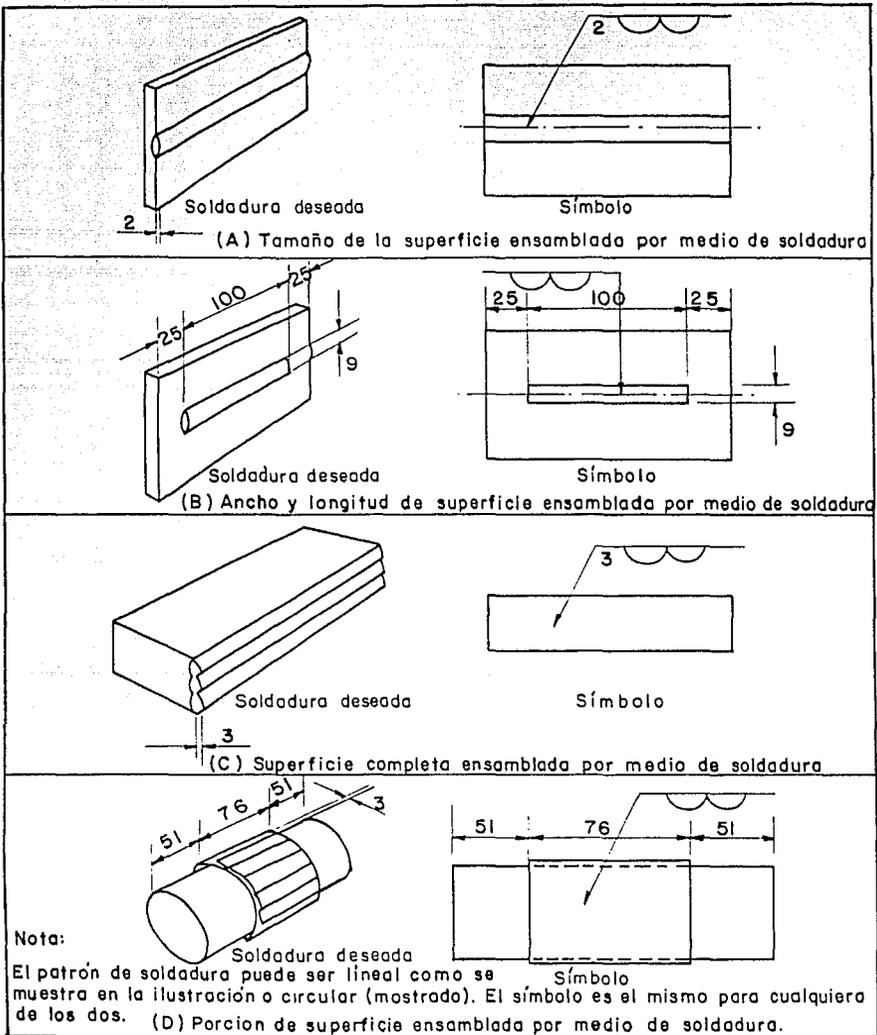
Aplicación del símbolo de soldadura de acabado para indicar superficie ensambladas por medio de soldadura
